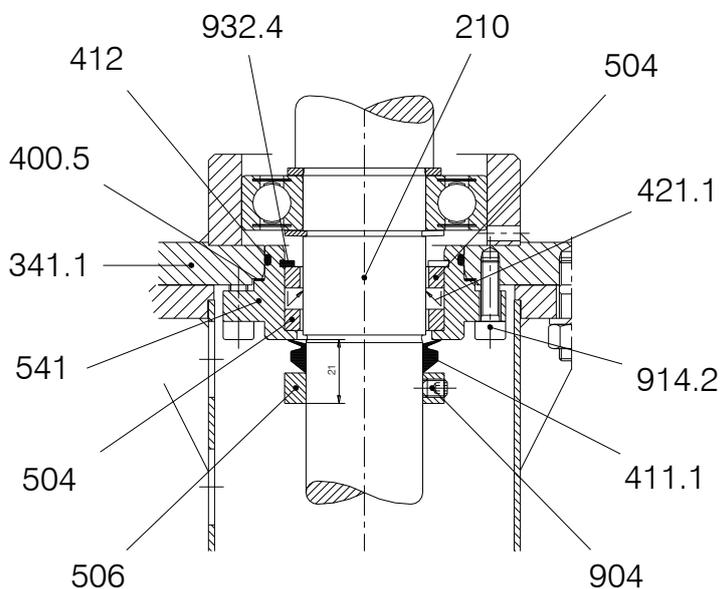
Detaillierte Montagezeichnung des Radialdichtrings
